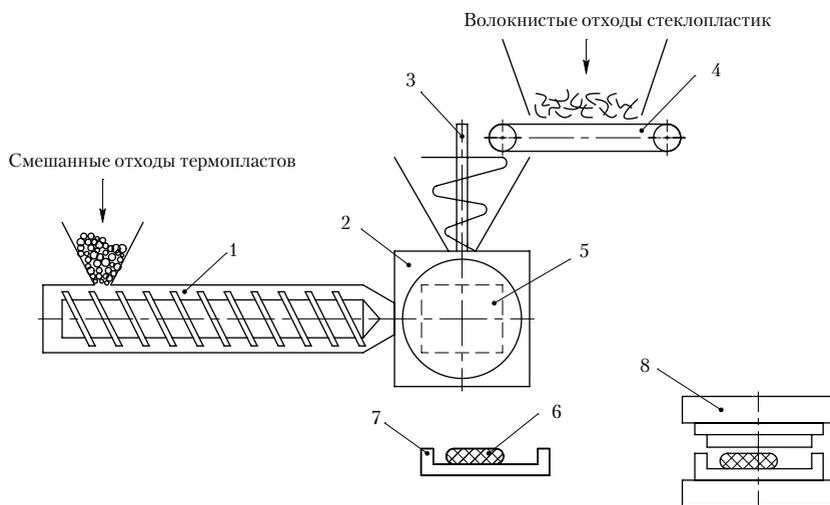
Схема процесса пласт-формования: 1 – червячный пластикатор, 2 – дисковый экструдер-смеситель (при необходимости), 3 – дозатор с коническим шнеком, 4 – ленточный транспортер, 5 – накопитель, 6 – заготовка, 7 – пресс-форма, 8 – гидравлический пресс.
